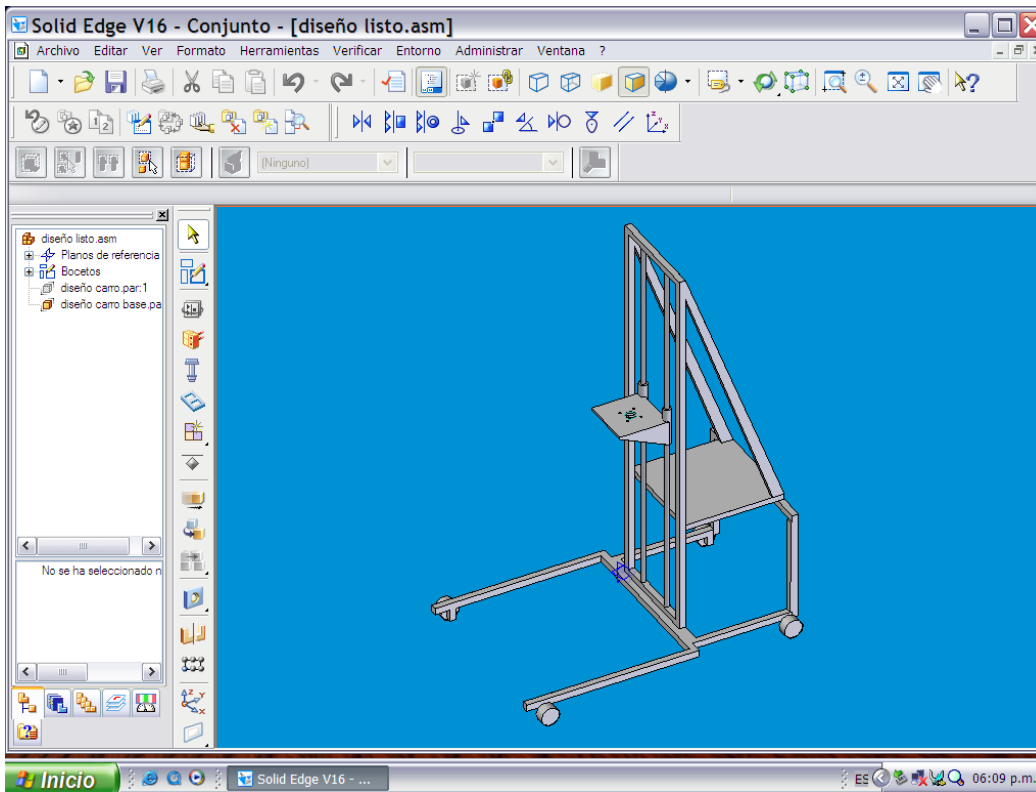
Diseño ensamblado del carro transportador de motor agitador
